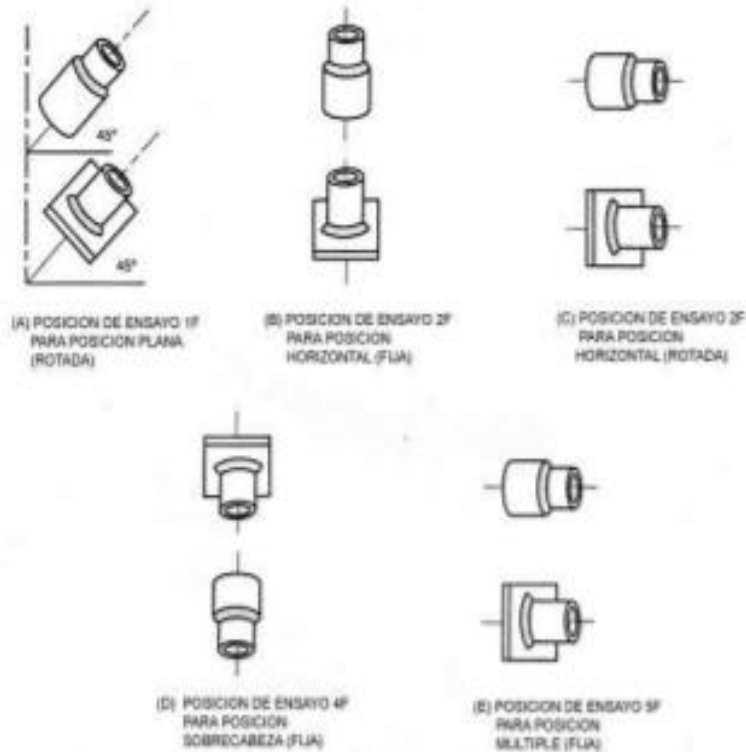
Posiciones de Tubos o Entubados de Ensayos para Soldaduras de Filete (ver 4.2.4)
